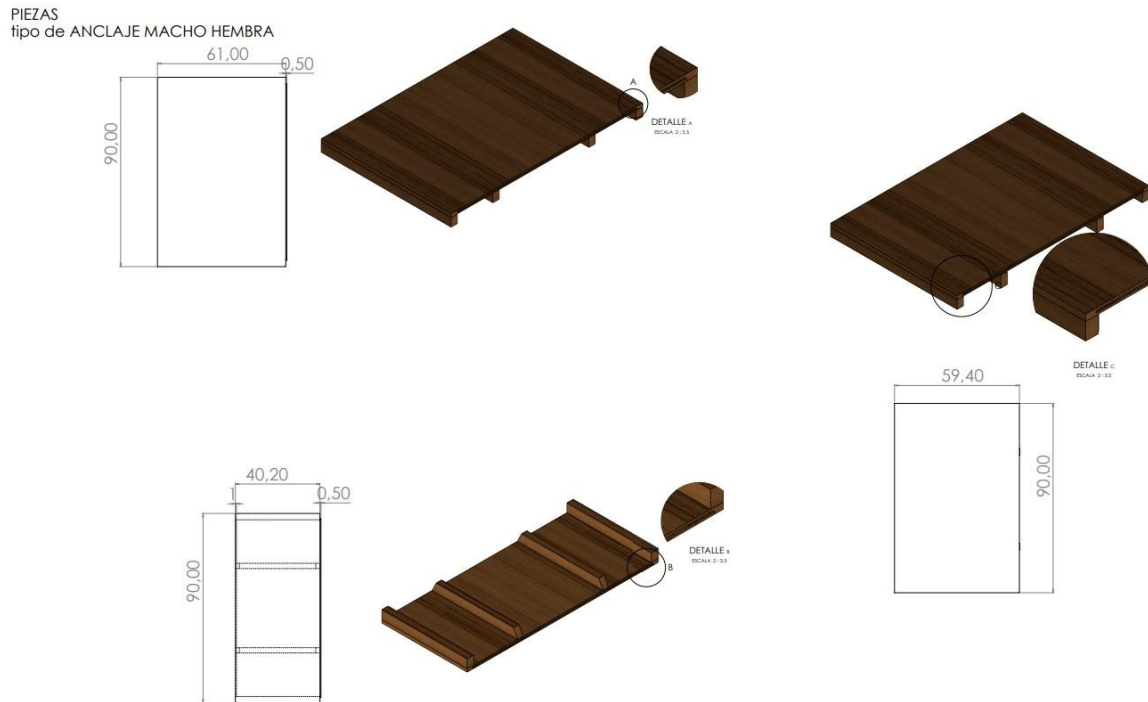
Plano comedor extensible (imagen). Muñoz A (2025)
